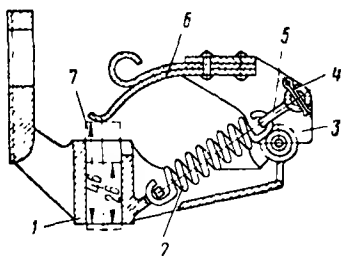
Щеткодержатель тягового двигателя ДК-106Б:
